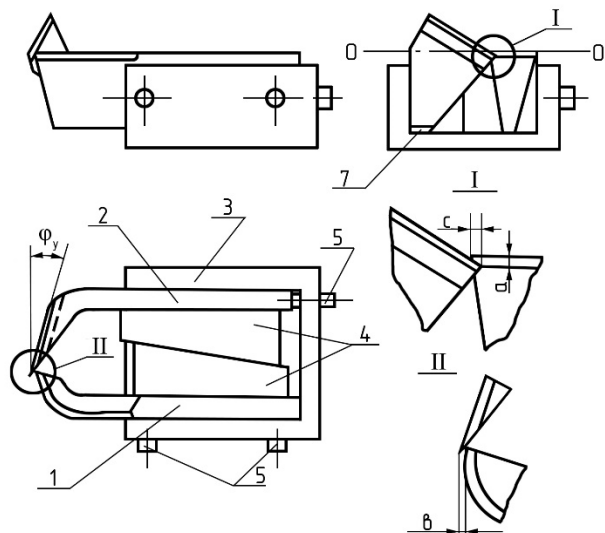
Конструкция резцовой головки с черновым и чистовым резцами
